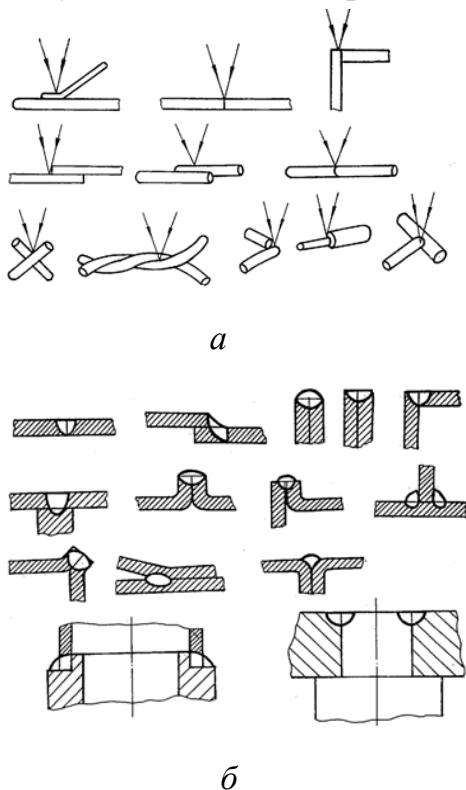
Типы соединений, выполняемых точечной (а) и шовной (б) лазерной сваркой
